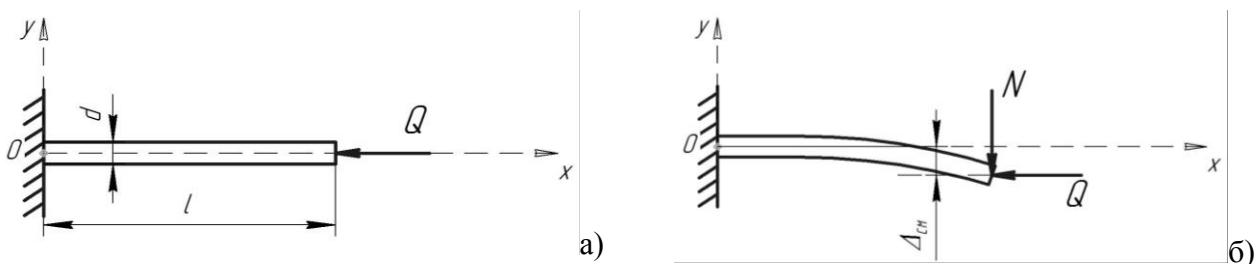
Схема закрепления и форма оправочного стержня под нагрузкой:
